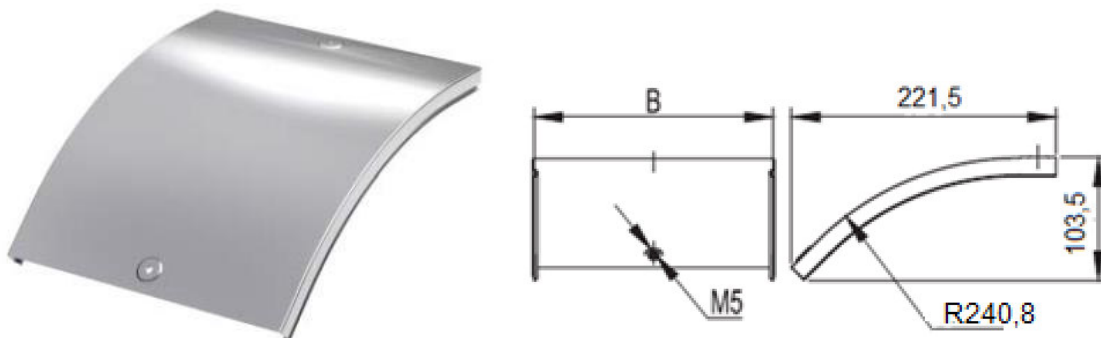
Крышка CD 45 на угол вертикальный внешний 45°, тип 3826
